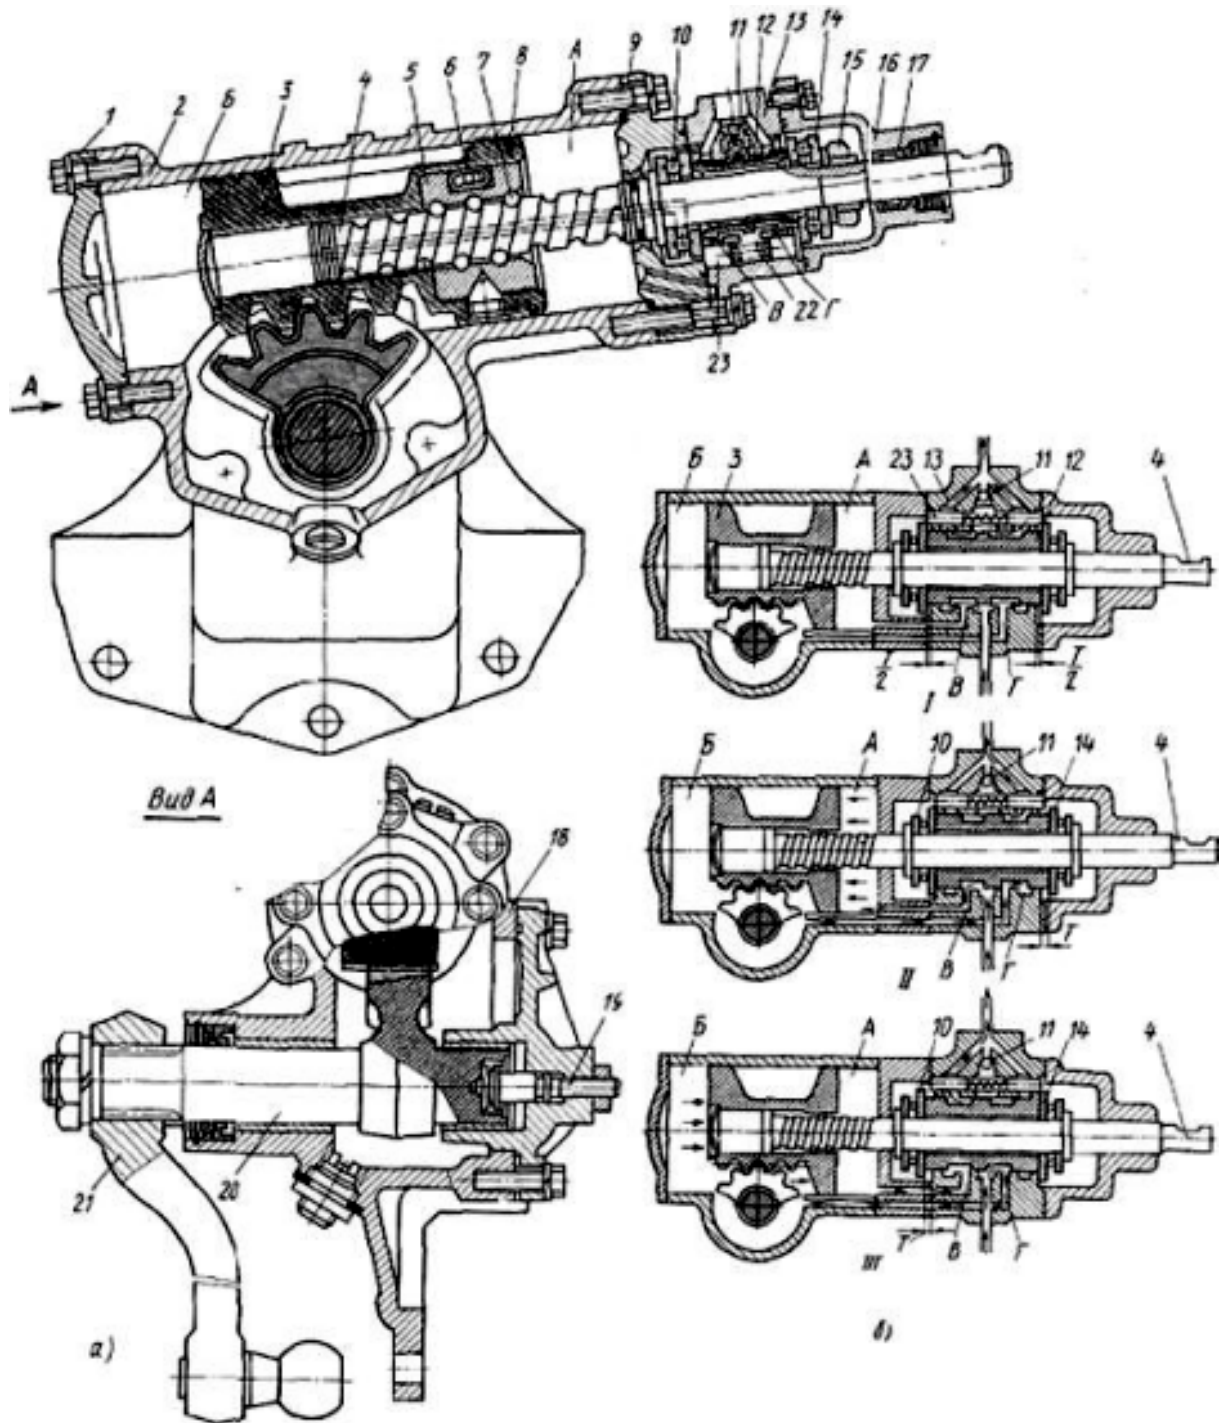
Рулевой механизм с гидроусилителем автомобиля ЗИЛ -130: а - конструкция; б - схема работы гидроусилителя; 1 - нижняя крышка; 2 - картер рулевого механизма; 3 - поршень-рейка; 4 - винт; 5 - шариковая гайка; 6 - желоб; 7 - шарик; 8 - поршневое кольцо; 9 - промежуточная крышка; 10 и 14 - упорные подшипники; 11 - шариковый клапан; 12 - золотник; 13 - корпус распределителя; 15 - гайка; 16 - верхняя крышка; 17 - роликовый подшипник; 18 - боковая крышка; 19 - регулировочный винт; 20 - вал рулевой сошки; 21 - сошка; 22 - центрирующая пружина; 23 - реактивный плунжер; I - при движении автомобиля по прямой; II - при повороте направо; III - при повороте налево
